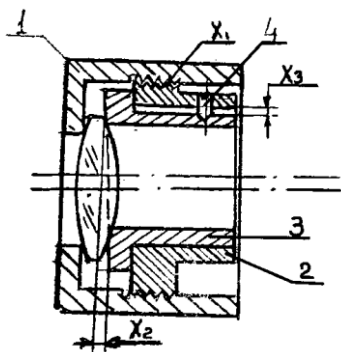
Оправа для проведения эксперимента: 1- корпус; 2 – резьбовое кольцо; 3 – стакан; 4 – винт
